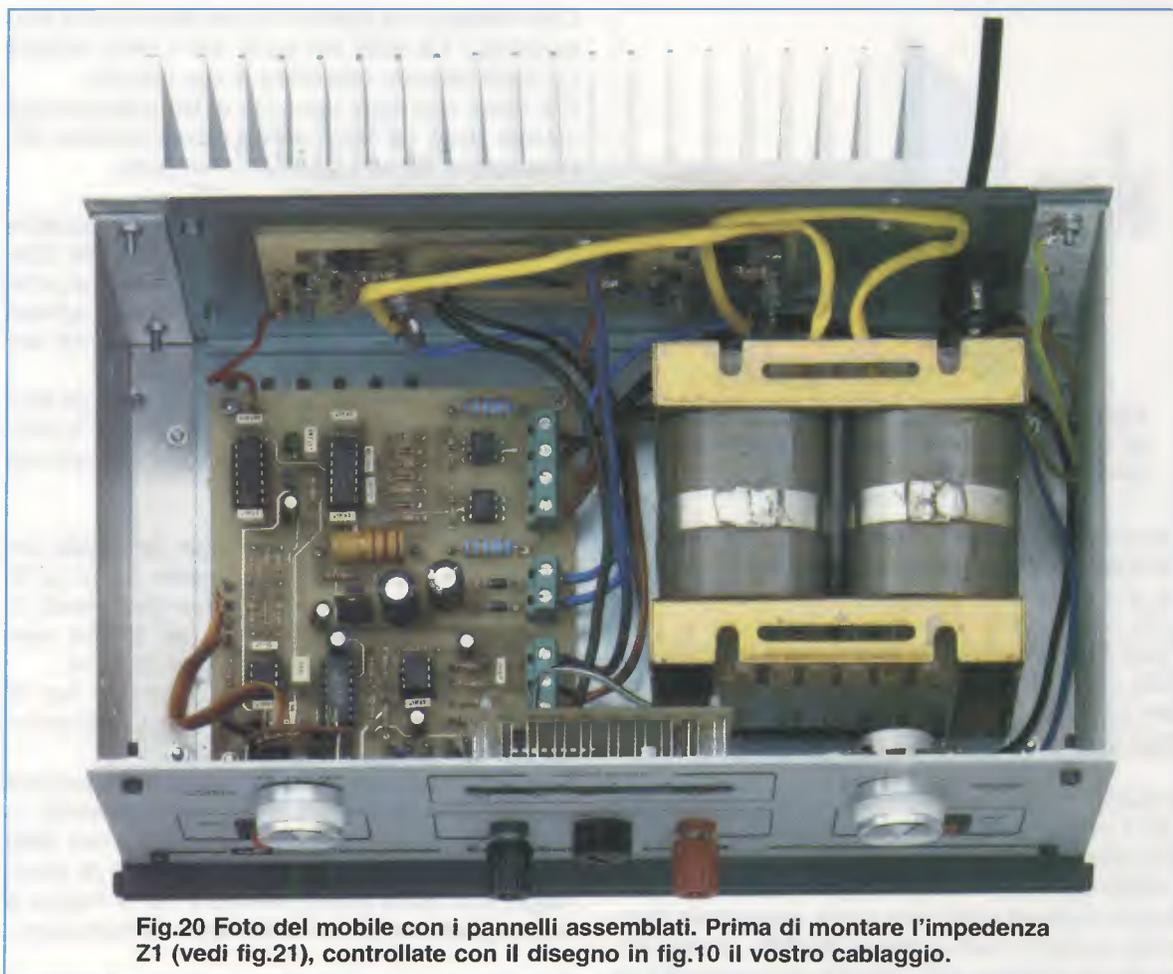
Foto del mobile con i pannelli assemblati. Prima di montare l'impedenza Z1 (vedi fig.21), controllate con il disegno in fig.10 il vostro cablaggio.
